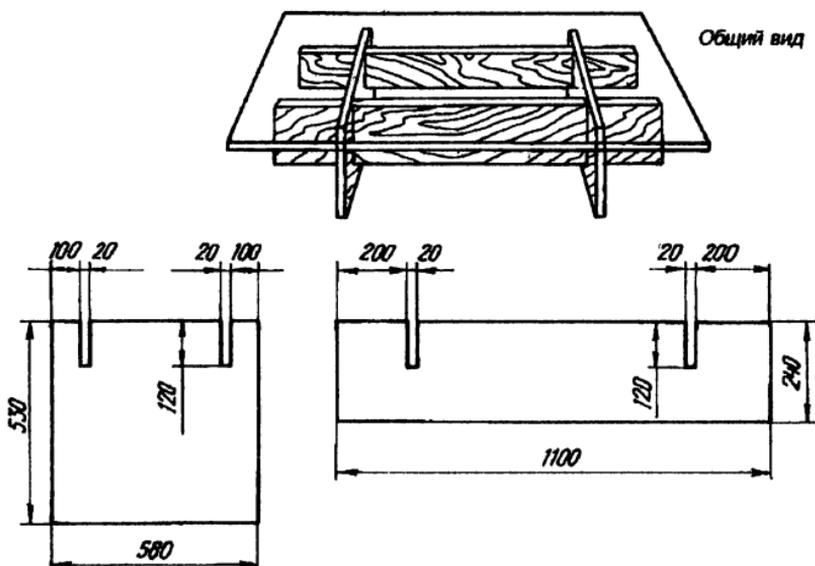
Журнальный столик со стеклянной столешницей: общий вид и сборочный чертеж
